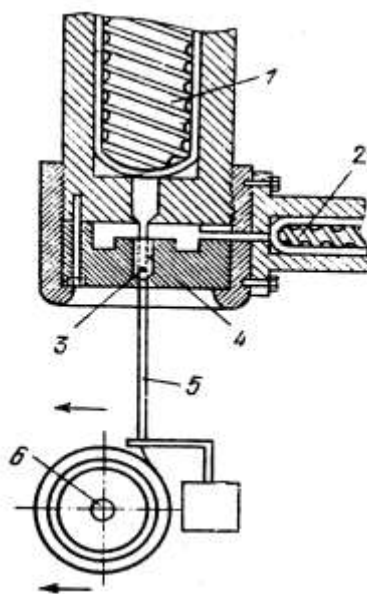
Схема плунжерной установки: 1 – плунжерный цилиндр с полимером для сердцевины; 2 – плунжерный цилиндр с полимером для оболочки; 3 – кольцевое фильерное отверстие; 5 – центральное фильерное отверстие; 6 – намоточный барабан
